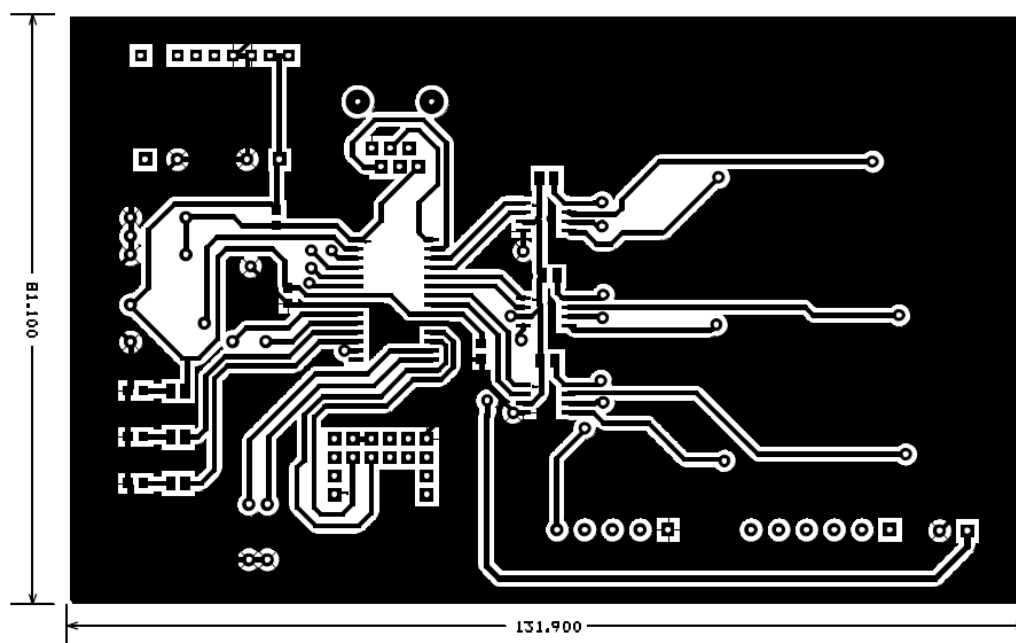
Vista da camada Top do PCB criado, com dimensões especificadas, em *mm*.
